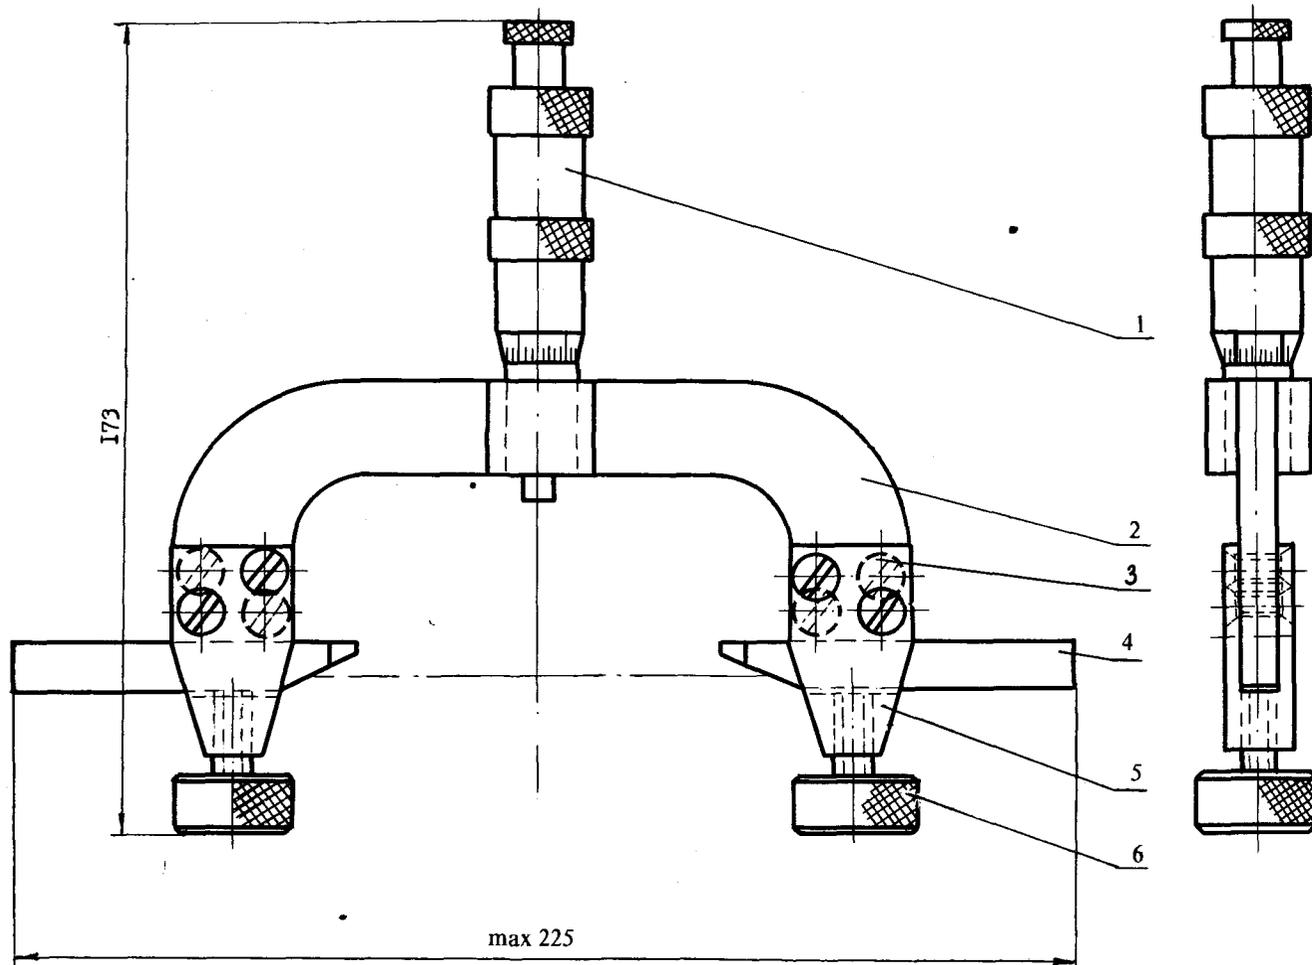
Калибр для проверки положения двух шпоночных пазов на валах:
